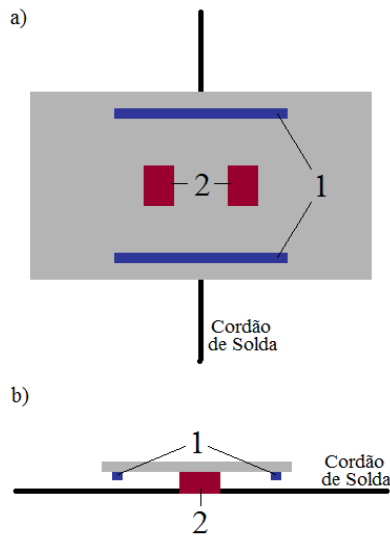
Posicionamento dos sensores para identificação (1) e ultra-sônicos (2) durante a inspeção. a) Vista superior b) Vista lateral esquerda.
